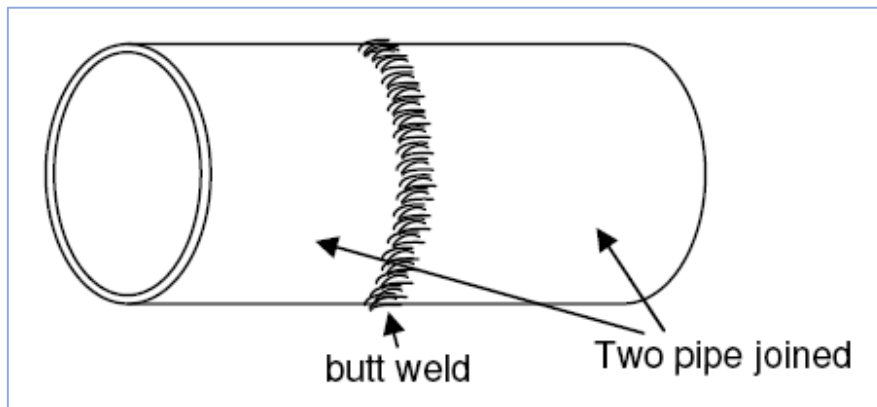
Schéma d'un assemblage de deux pipes en bout à bout [48]
